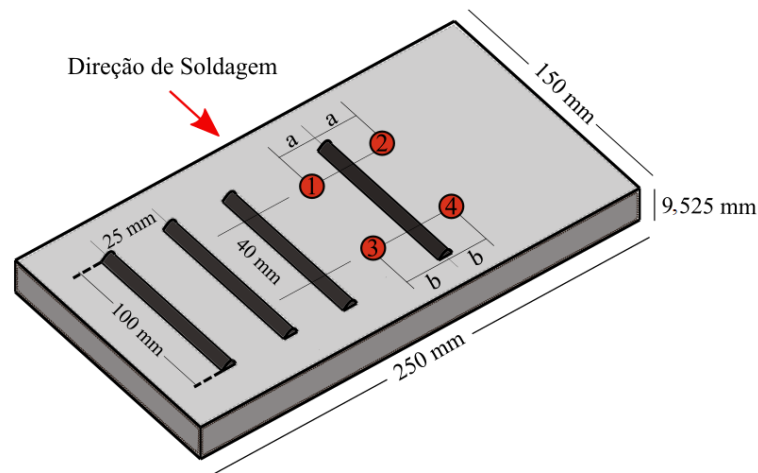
Configuração dos cordões de solda. Fonte: Autor.
